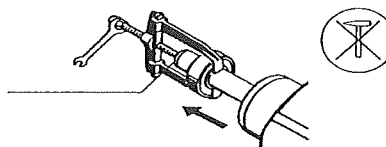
Lagerwechsel / Changing bearings / Remplacement des roulements / Cambio de cojinetes / Sostituzione del cuscinetto / Lagerbyte
